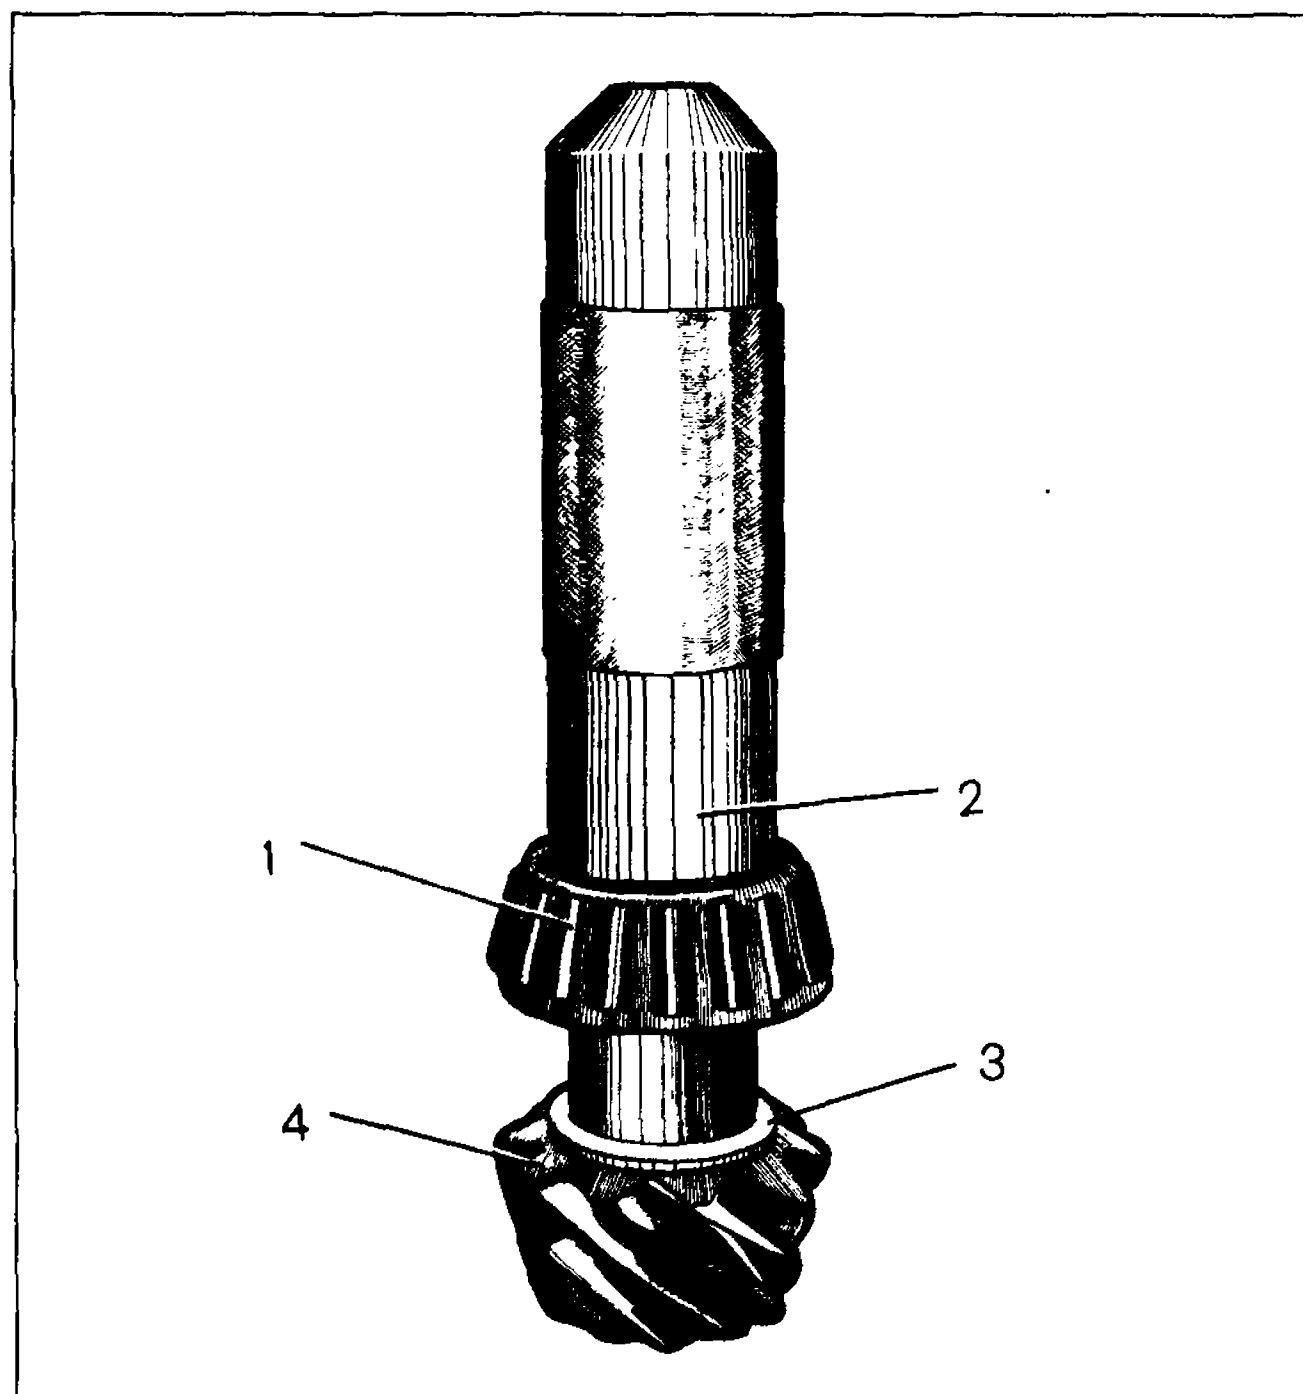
Установка внутреннего кольца заднего подшипника на ведущую шестерню:
